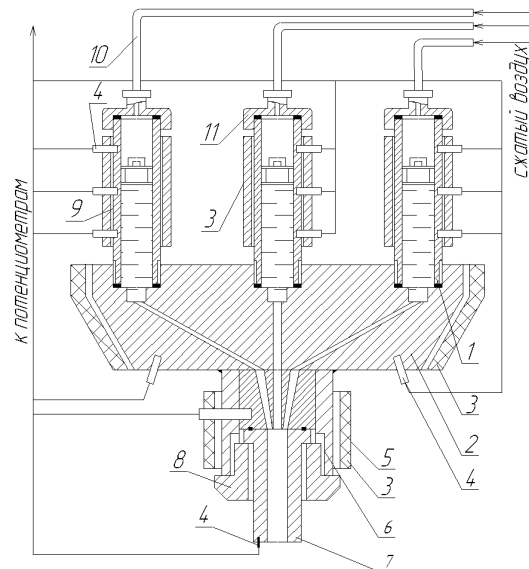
Схема экспериментальной установки для изучения соэкструзии комбинированных расплавов полимеров: 1 - цилиндр высокого давления; 2 - соединительный блок; 3 - нагревательные элементы; 4 - термopара; 5, 6 - блок питания; 7 - канал; 8 - прижимная гайка; 9 - поршень; 10 - патрубок; 11 - крышка цилиндра
